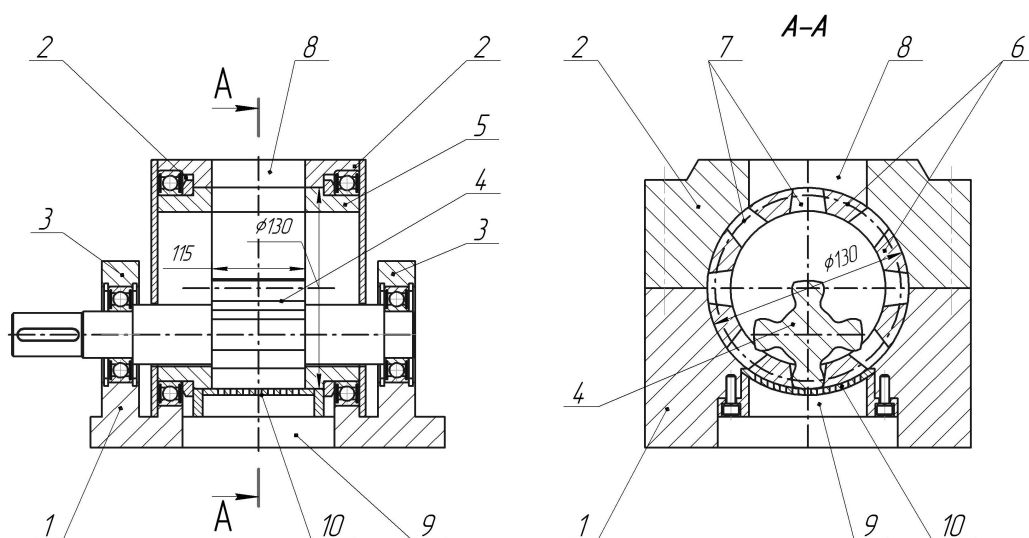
Конструкция измельчителя на основе цилиндрической зубчатой передачи (обозначения см. в тексте)
